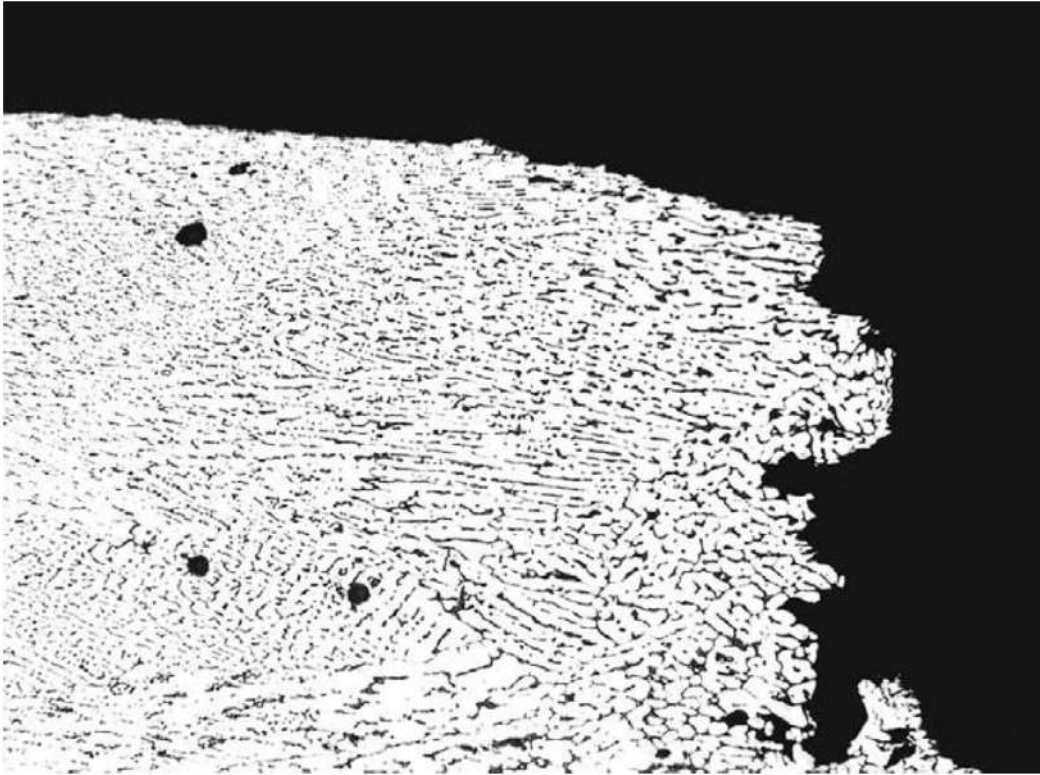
Detalle mostrando la falta de fusión en la región de inicio de la fractura de soldadura del tubo 1. Ácido fluorídrico (0.5%). 100X.
